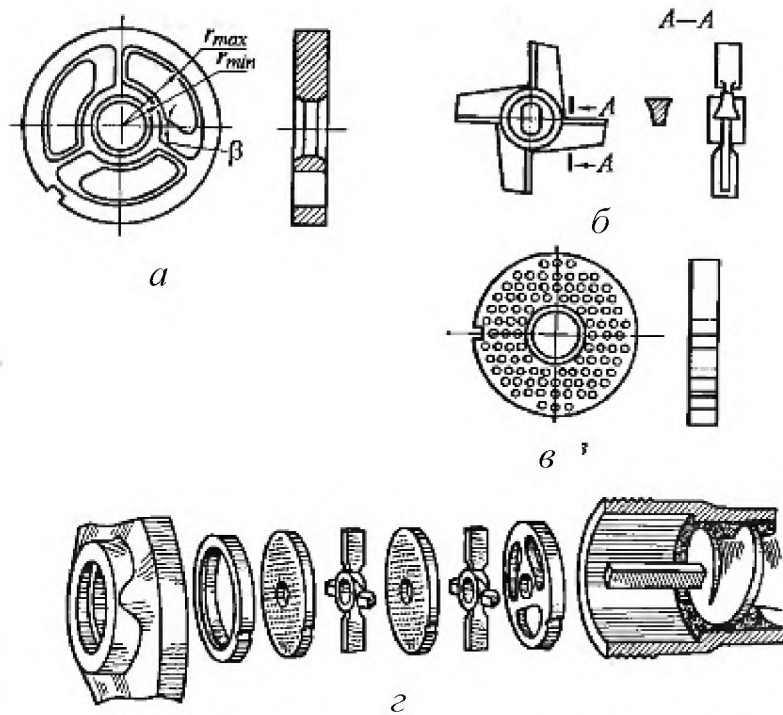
Різальні інструменти м'ясорубок: 1 – нерухома підрізна решітка; б – двосторонній ніж, що обертається; в – решітка ножова; г – основний набір різальних інструментів
